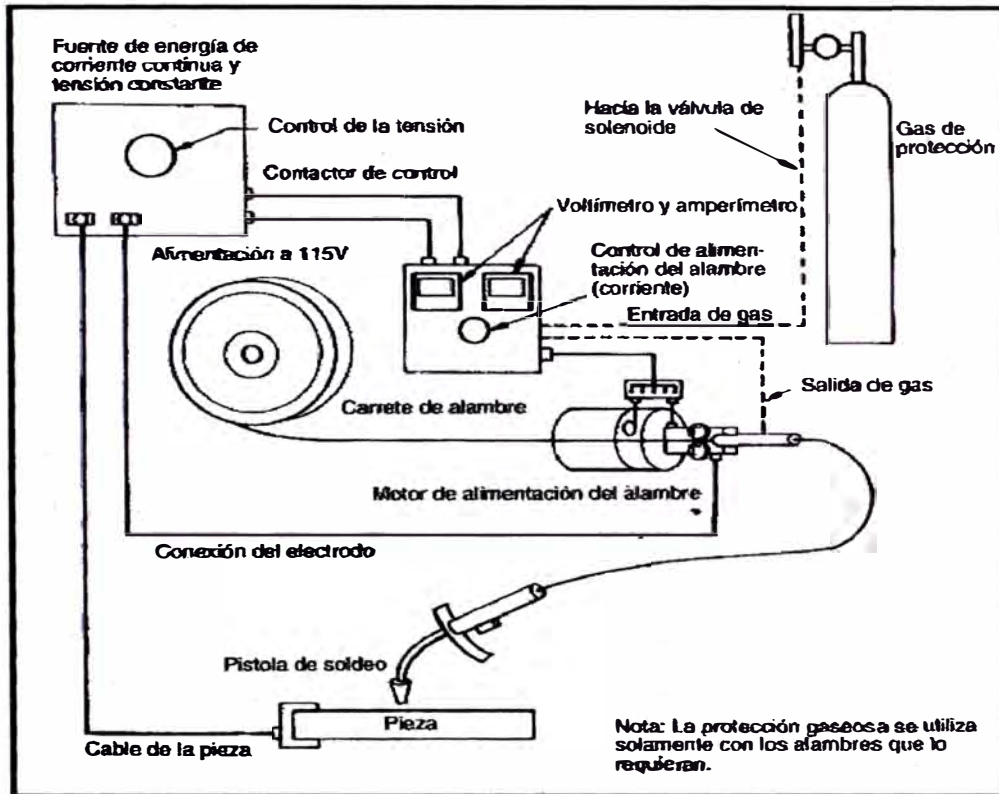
Equipo para el soldeo por arco con alambre tubular
